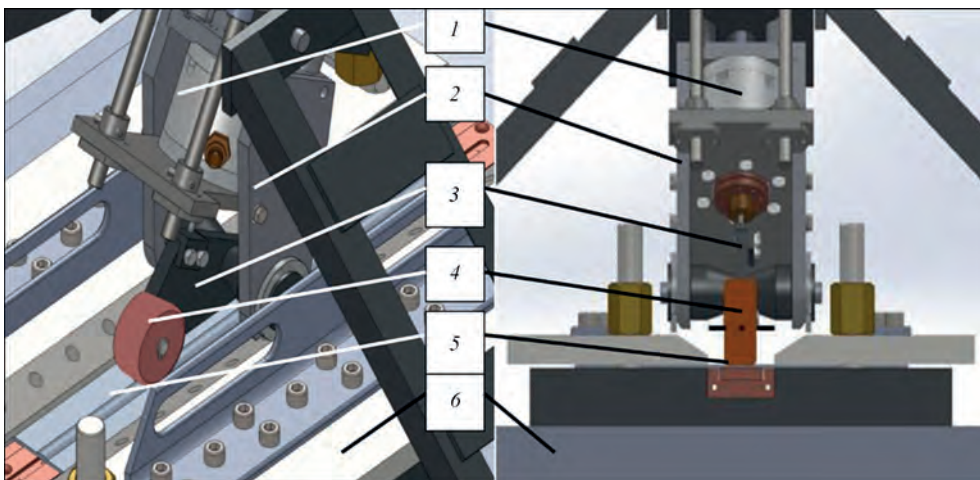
Варіант конструктивної схеми контакту електрода ЕДО у формі ролика з металом зварного шва: 1 – індуктор лінійного переміщення; 2 – корпус кріплення ролика; 3 – система фіксації ролика; 4 – електрод ЕДО; 5 – зварне з'єднання; 6 – збиральна плита
